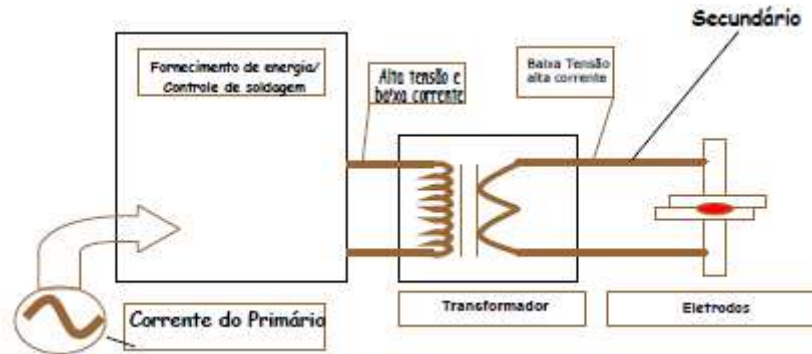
Circuito elétrico típico máquina de solda a ponto[28].
